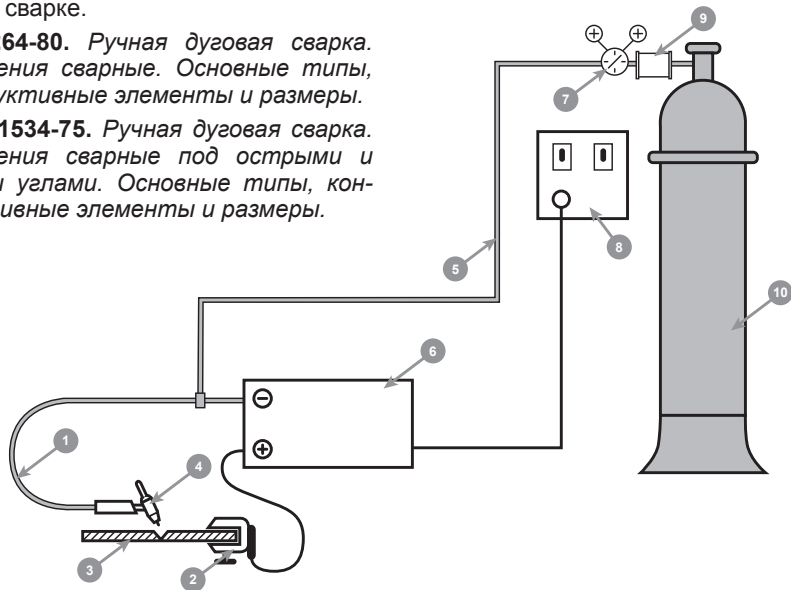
Схема подключения сварочного аппарата в режиме TIG LIFT-сварки.
